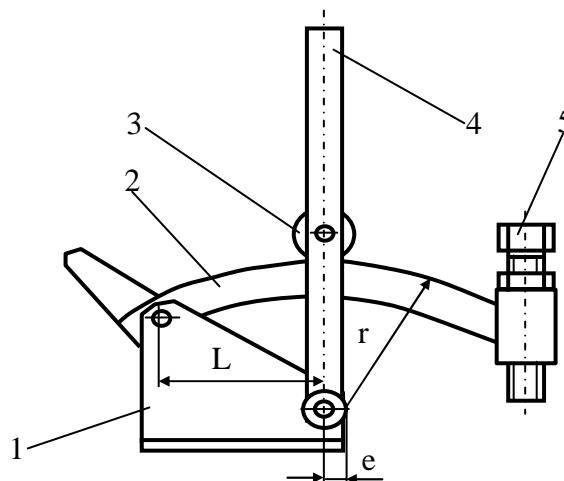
Ексцентриковий притискач з великим робочим ходом (дуговий притискач): 1-корпус; 2-дуга; 3-ролик; 4-рукоятка; 5-гвинт регульовальний.
